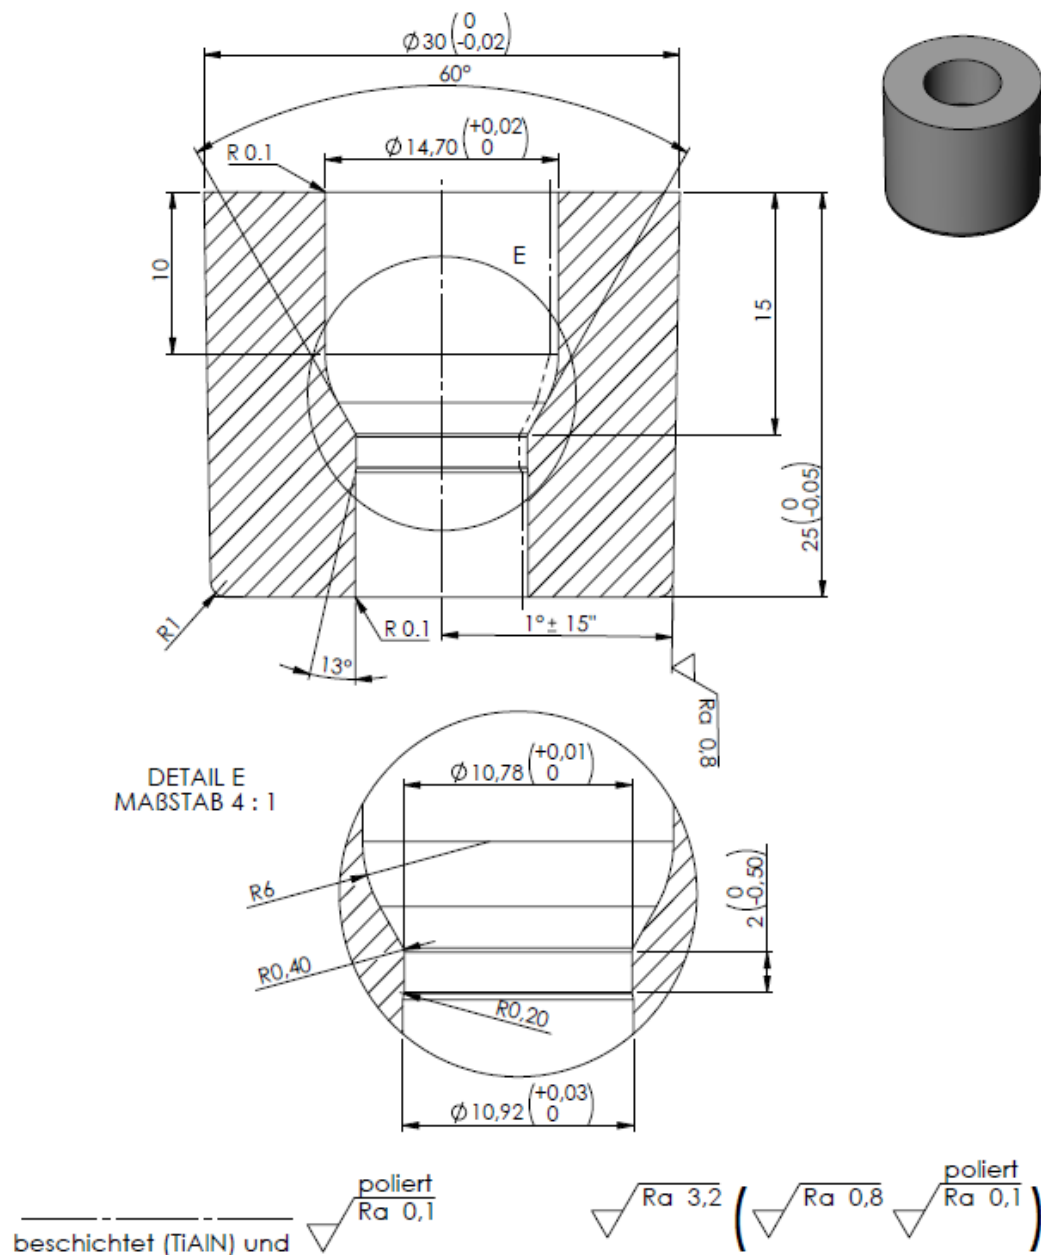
Technische Zeichnung der Umformmatrize für das Fließpressen.
